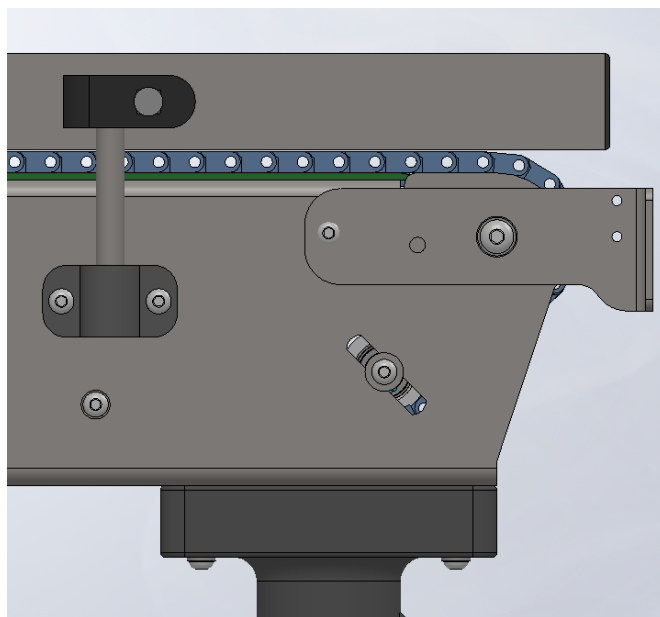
Зовнішній вигляд вузла натяжного ролика
